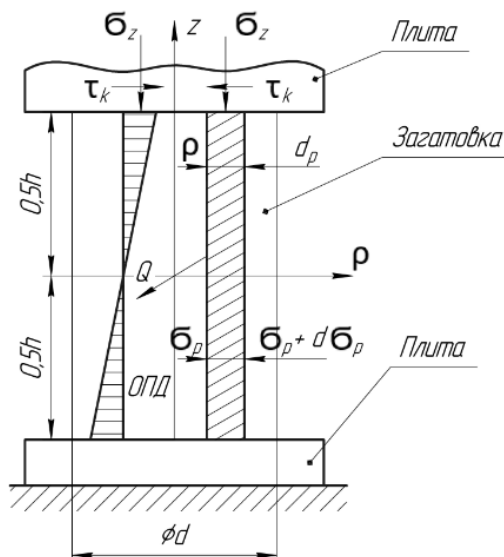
Расчетная схема при осадке цилиндрической заготовки
